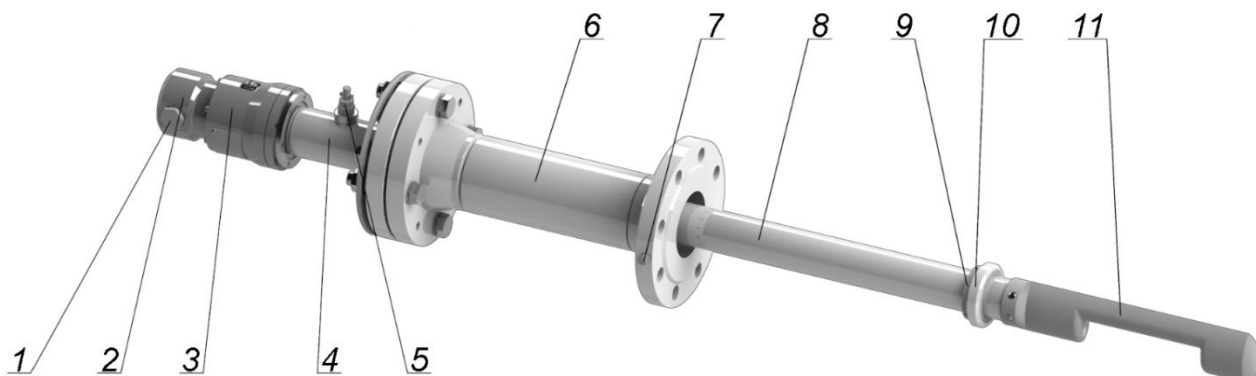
Приемопередатчик М ЛБ, без установочного приспособления
